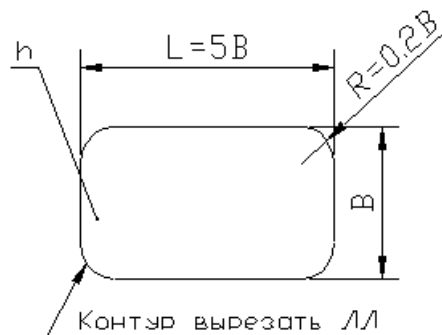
Эскизы деталей, обрабатываемых лазерным лучом (ЛЛ); пластина из листового материала
